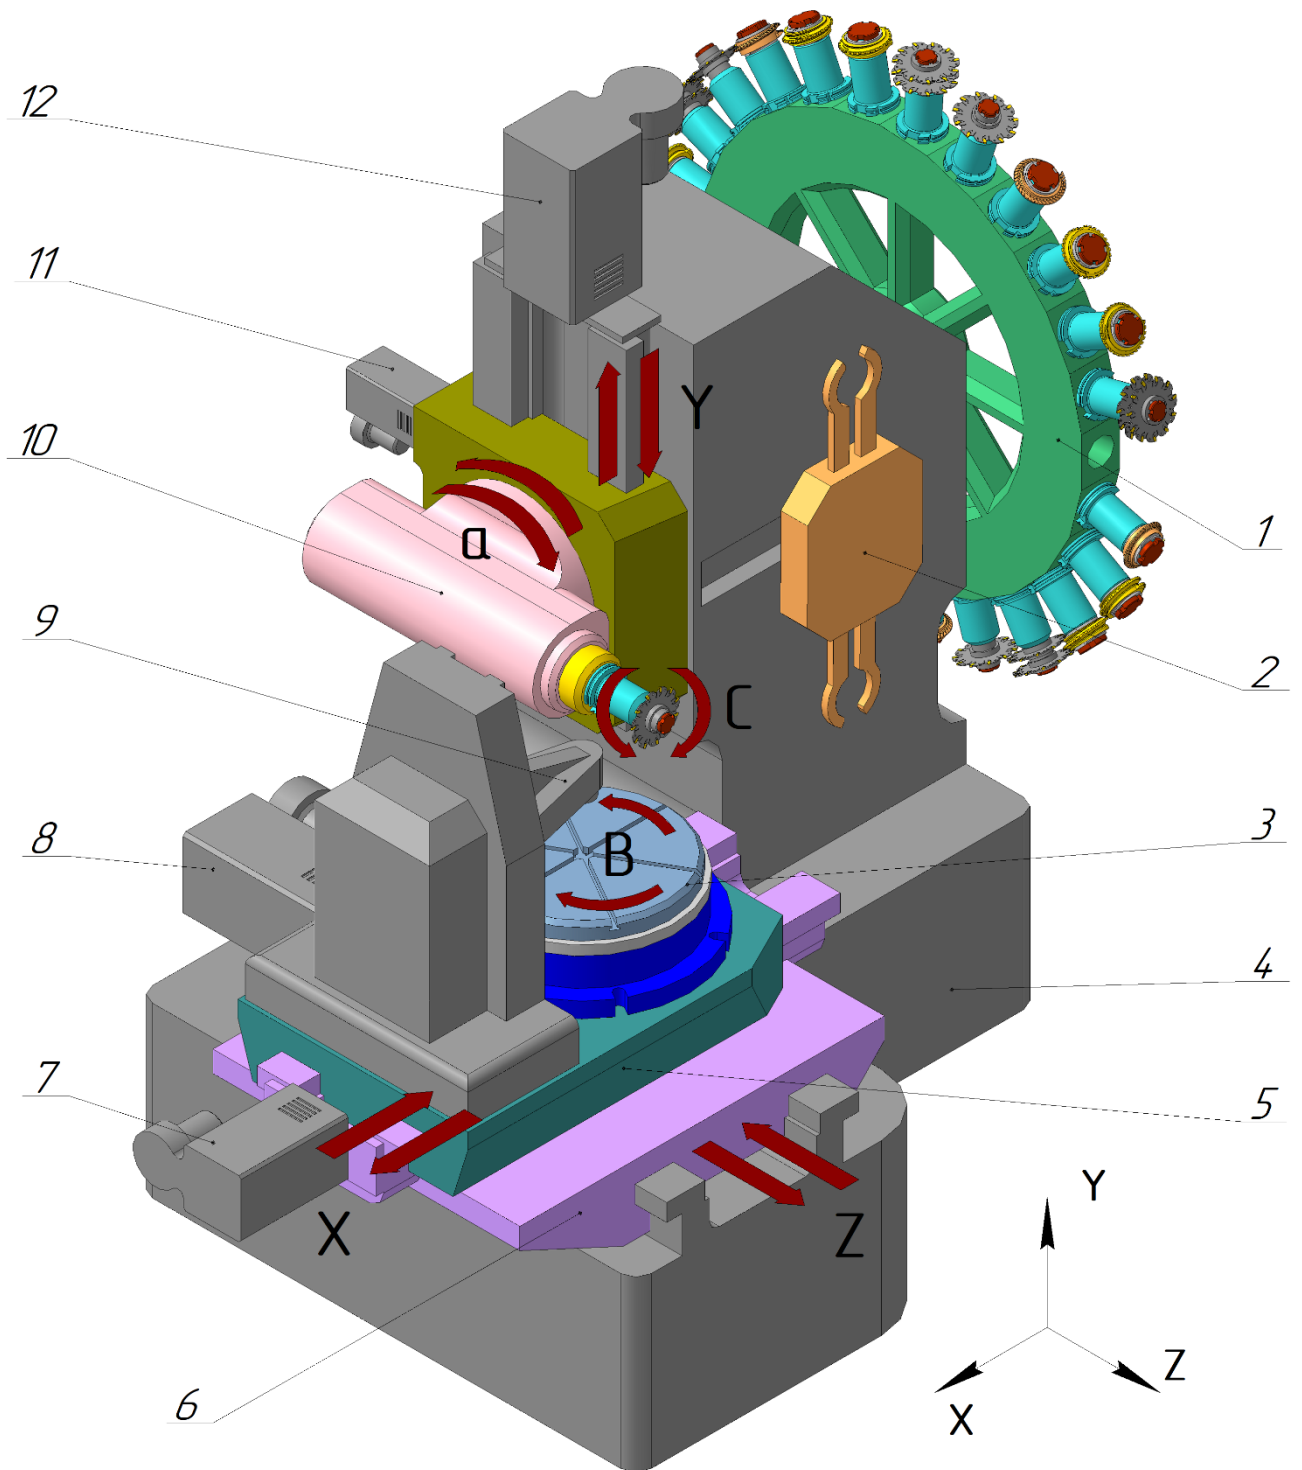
Компоновка верстата для здійснення зубообробки
